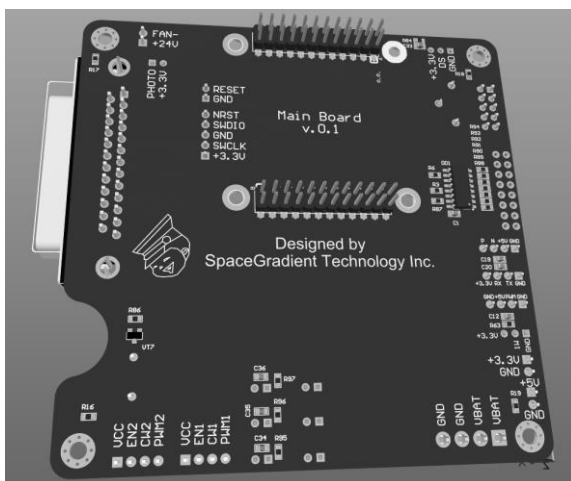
3D-модель печатной платы устройства (нижняя сторона)
